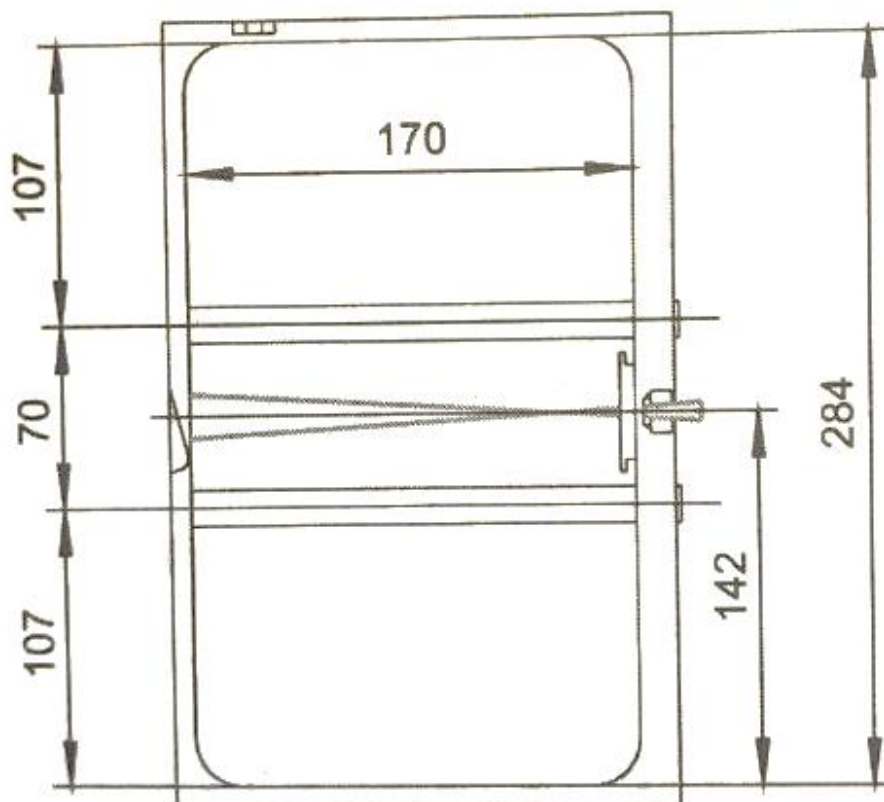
Рабочая камера SPECORD 40 (вид сверху)
